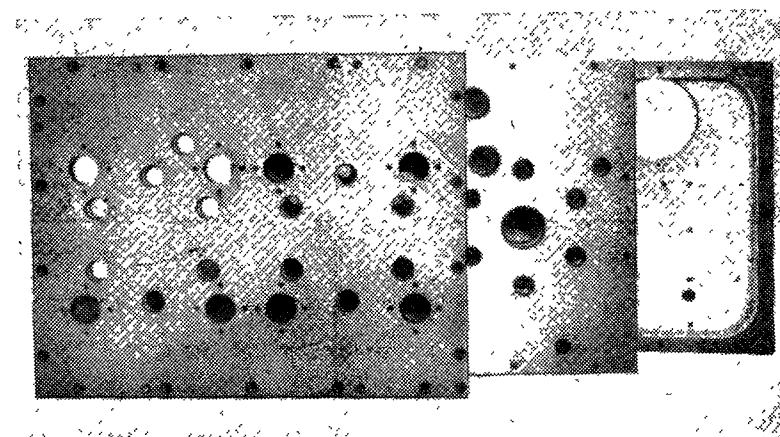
Корпусные детали многошпиндельной коробки после механической обработки
